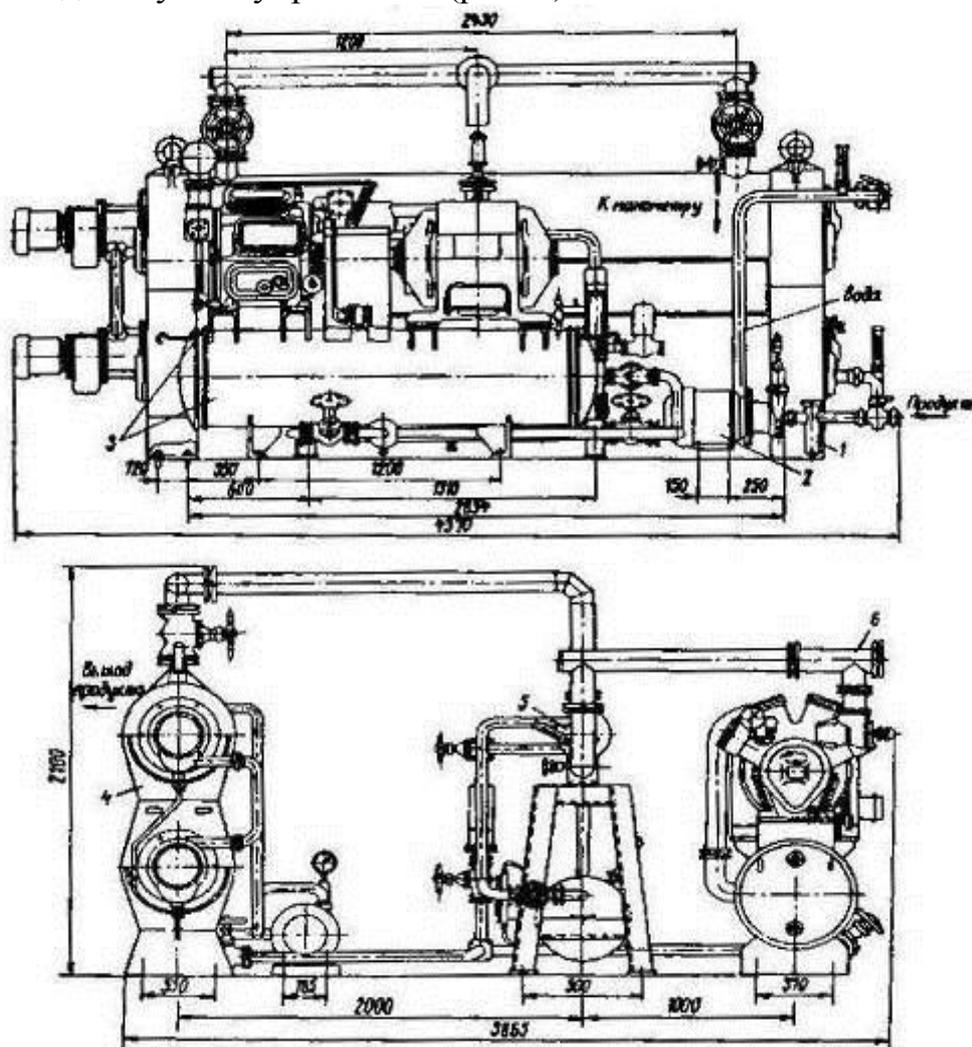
Установка для непосредственного охлаждения вин и виноматериалов ВУНО-90: 1 – продуктовый фильтр; 2 – центробежный электронасосный агрегат ВЦН-20 ; 3 – компрессорно-конденсаторный агрегат АК-ФУУ-80-11А; 4 – испаритель-охладитель ВОИ-58; 5 – теплообменник ТФ-80-1А; 6 – угловой фреоновый фильтр УФФ-100А
